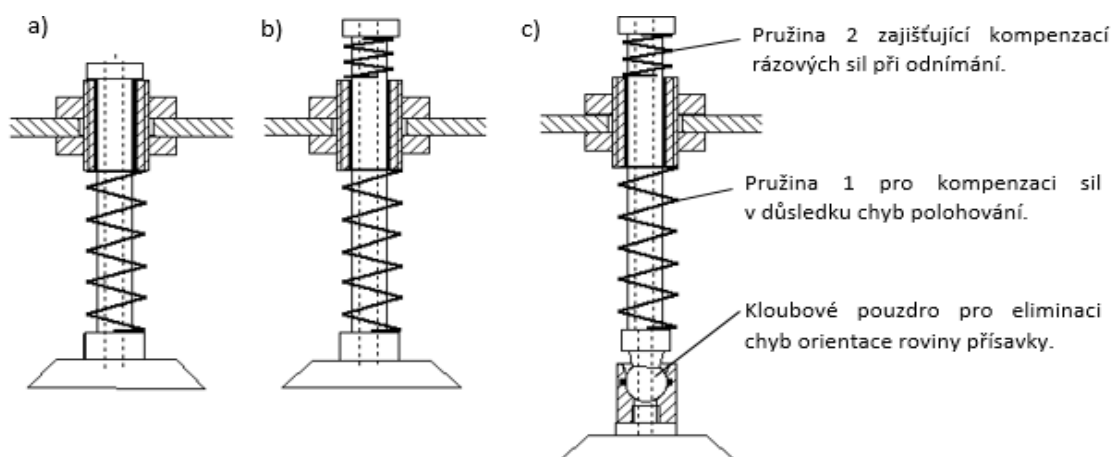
Konstrukce APÚH s jednou přísavkou
